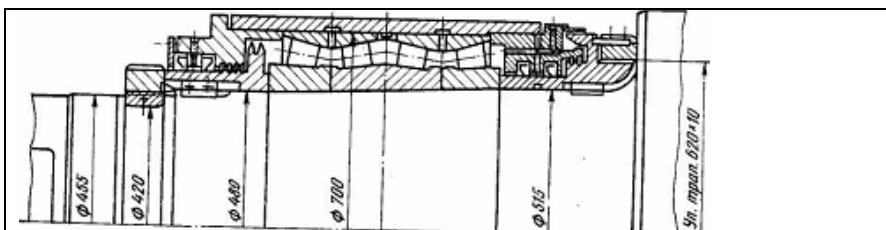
Конструкция подшипникового узла рабочего валка с конической шейкой на роликовых конических подшипниках четырех валкового стана 2000
